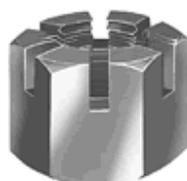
Ilustração Porca Castelo. Fonte IRIGAR Materiais de Construção.
